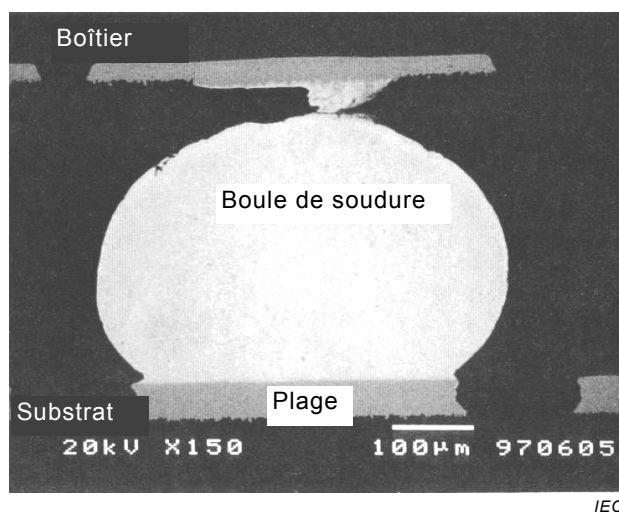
Soudure défectueuse en raison d'une coupure de la boule de soudure
